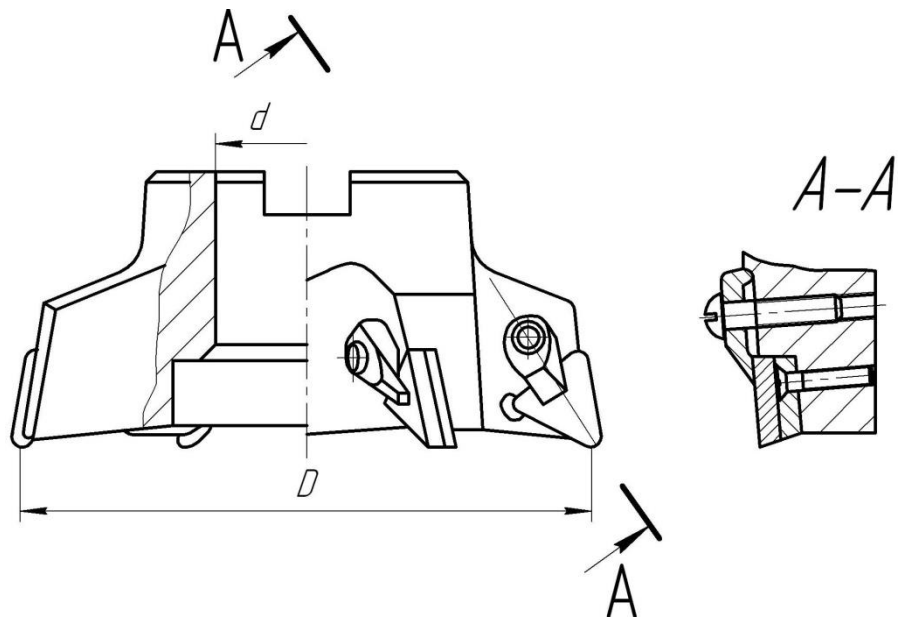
Фреза торцева фірми “USAP” (Італія)
